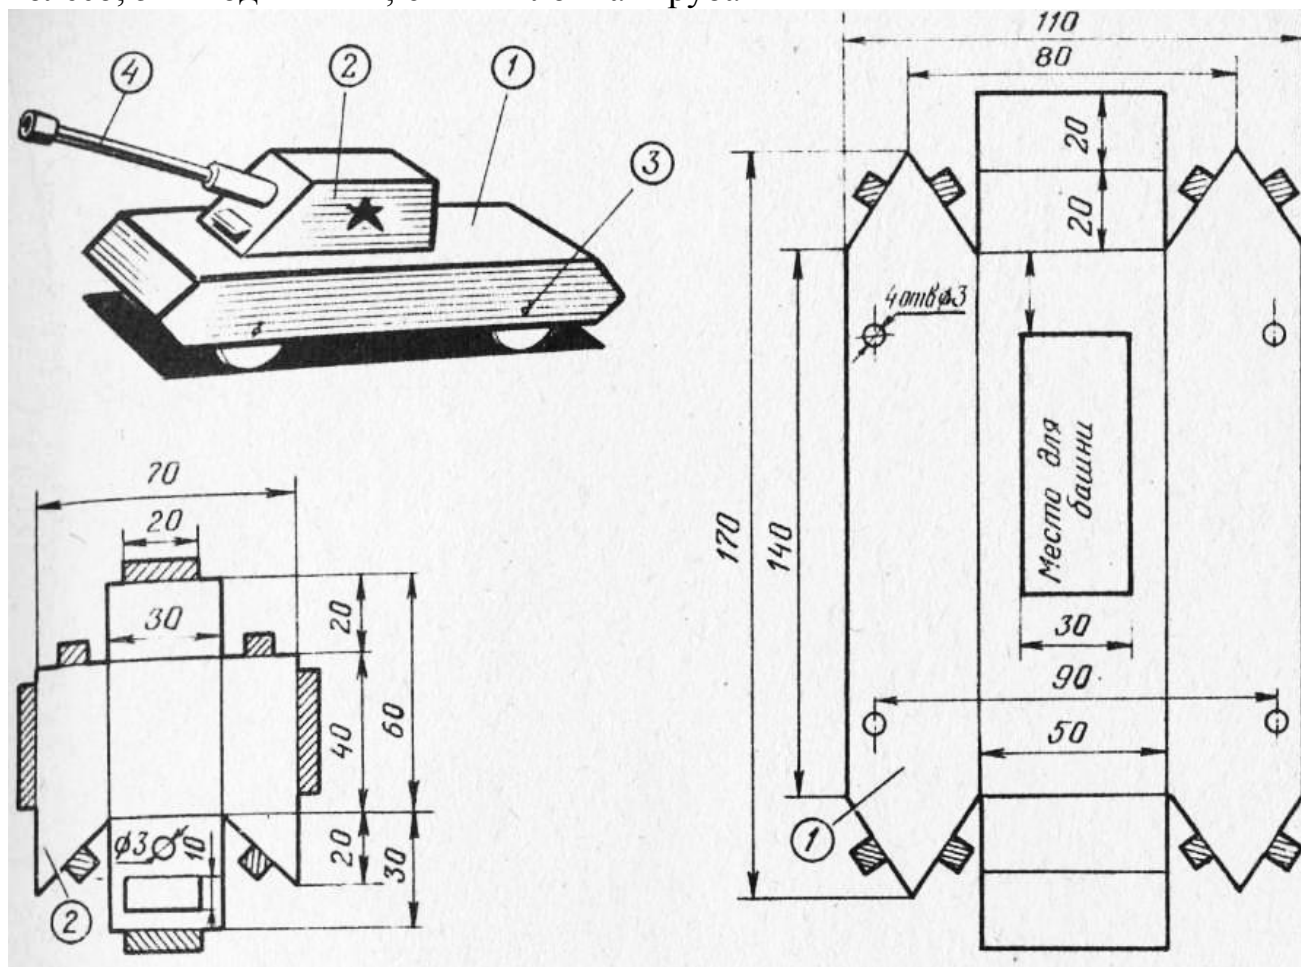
Модель танка: 1 — корпус; 2 — башня; 3 — ось; 4 — ствол
